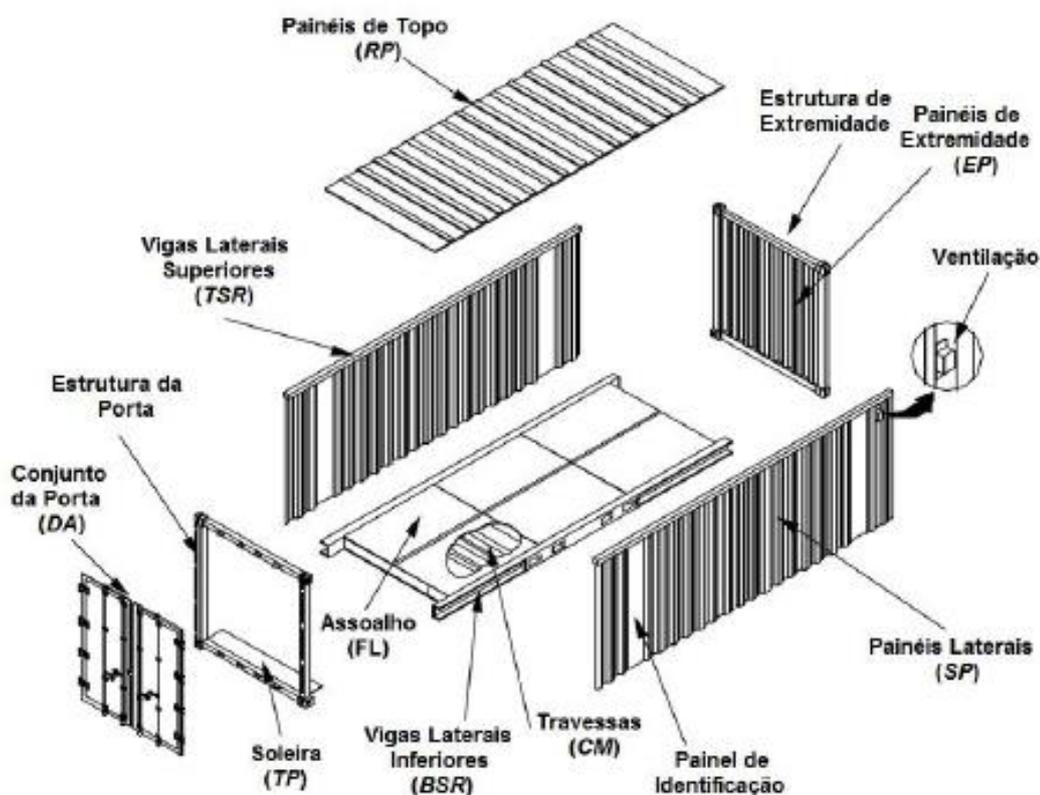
Perspectiva dos conjuntos estruturais de um contêiner
